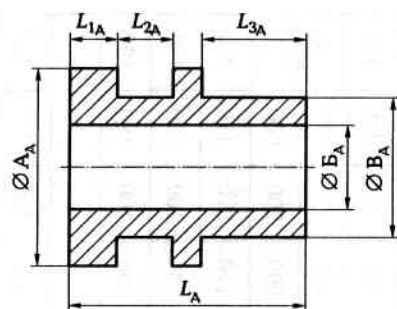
Эскиз обрабатываемой детали (втулки)
